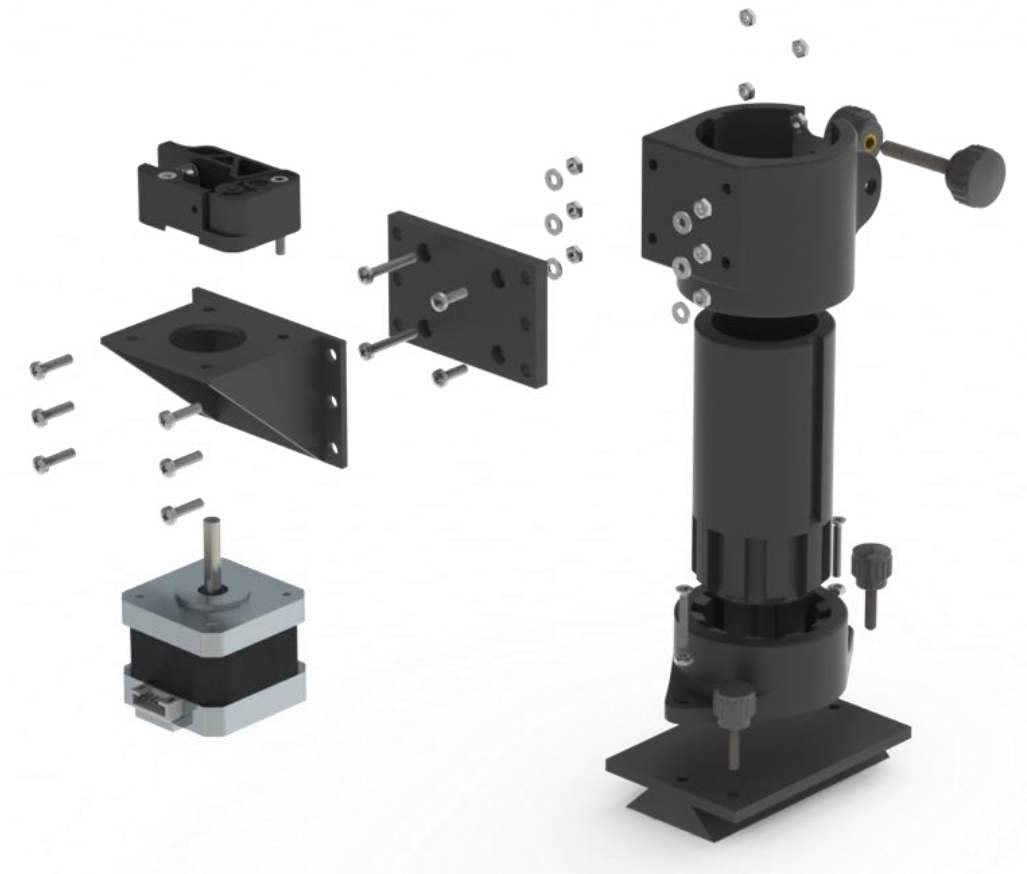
Vista explosionada del subconjunto 1. Fuente: propia
